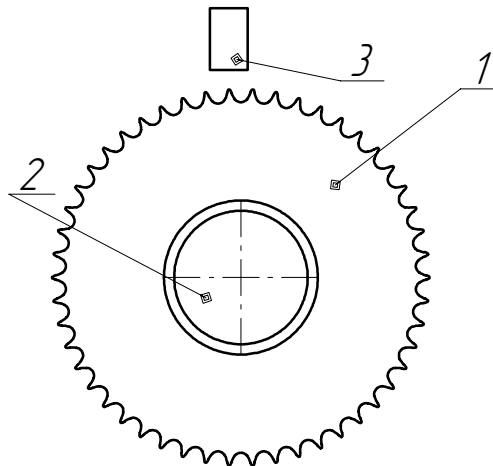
Схема конструкции магнитоэлектрического преобразователя
